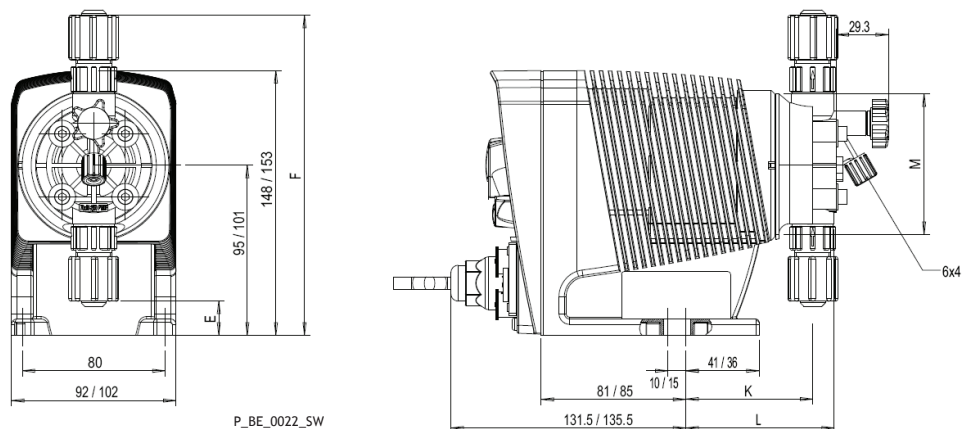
Размерный чертеж Beta® BT4b/BT5b, Материал конструкции PV – размеры в мм
